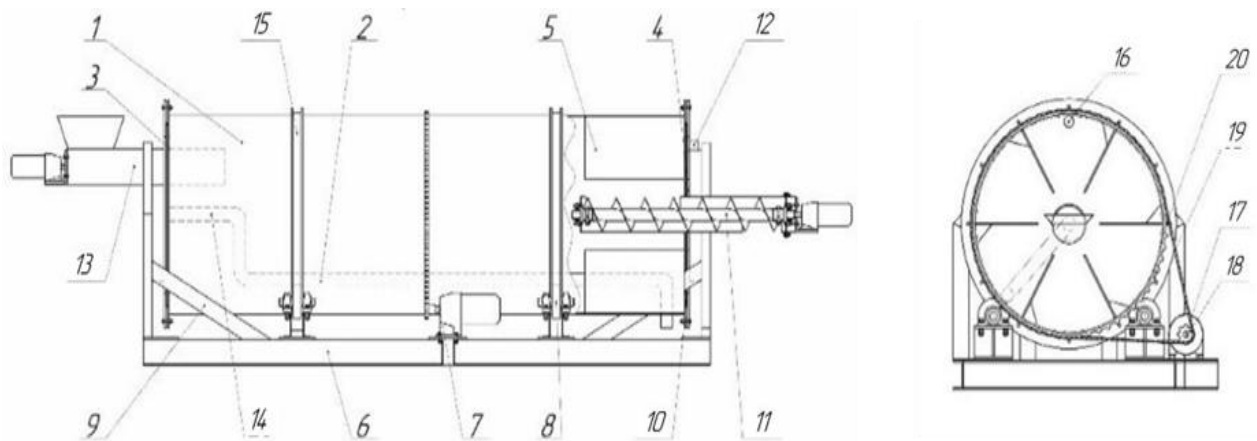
Схема устройства биореактора барабанного типа:
